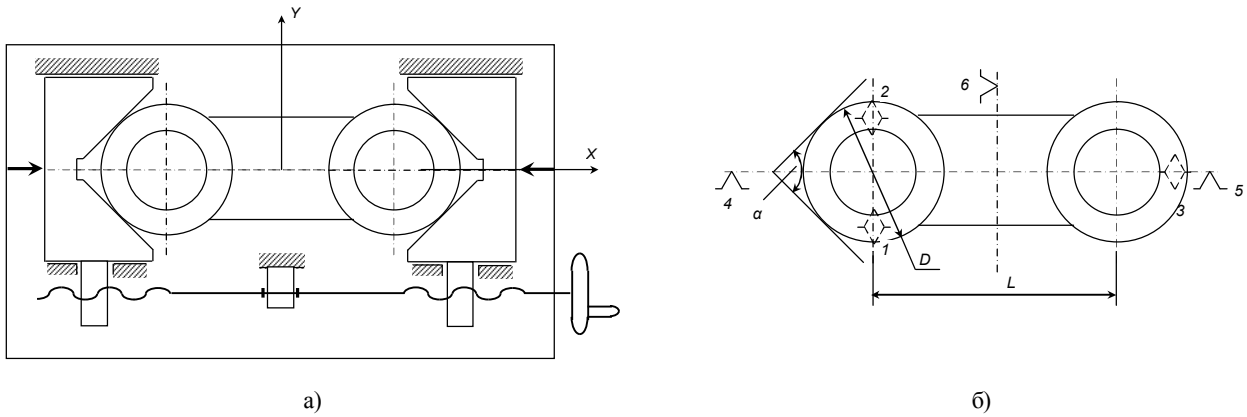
Конструктивна схема верстатного пристрою за варіантом 2 з установленою вихідною заготовкою (а) і схемою базування (б)
